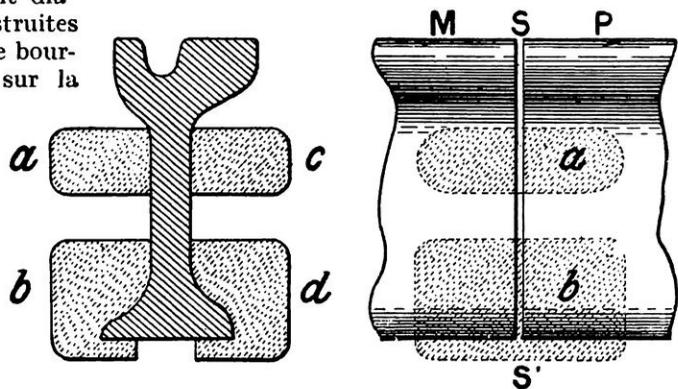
SOUDURE DES RAILS PAR COURT-CIRCUIT
